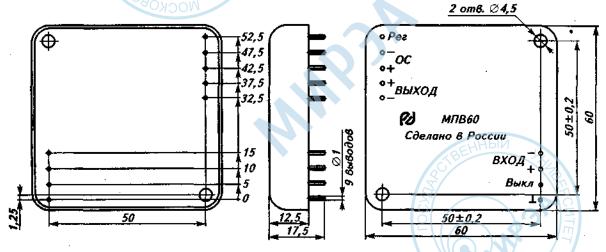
Общий вид, габаритные и присоединительные размеры модулей питания МПВ60 и МПЕ60
